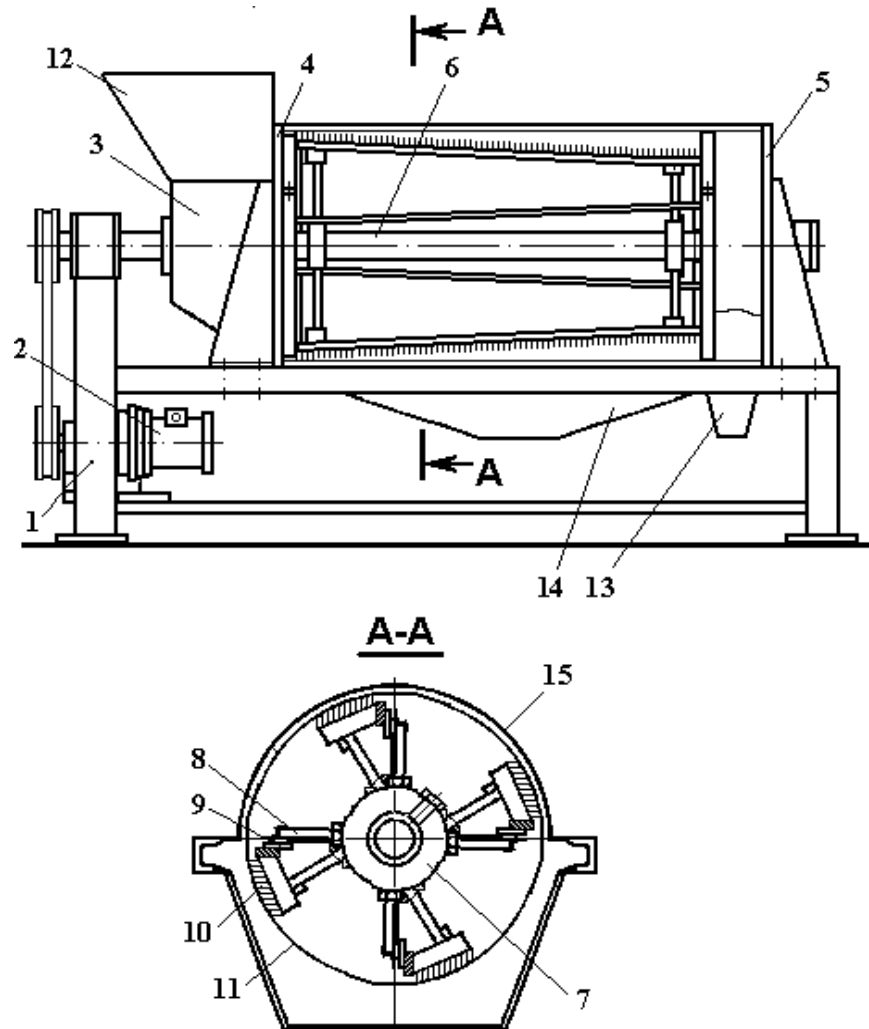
Конструктивно-технологічна схема щіткового роторного просіювача: 1 – рама; 2 – привод; 3 – корпус; 4, 5 – боковини; 6 – вал; 7 – бобишка; 8 – палець; 9 – пластина; 10 – щітка; 11 – сито; 12 – завантажувальна горловина; 13 – вивантажувальна горловина; 14 – вивантажувальне вікно; 15 – кожух
